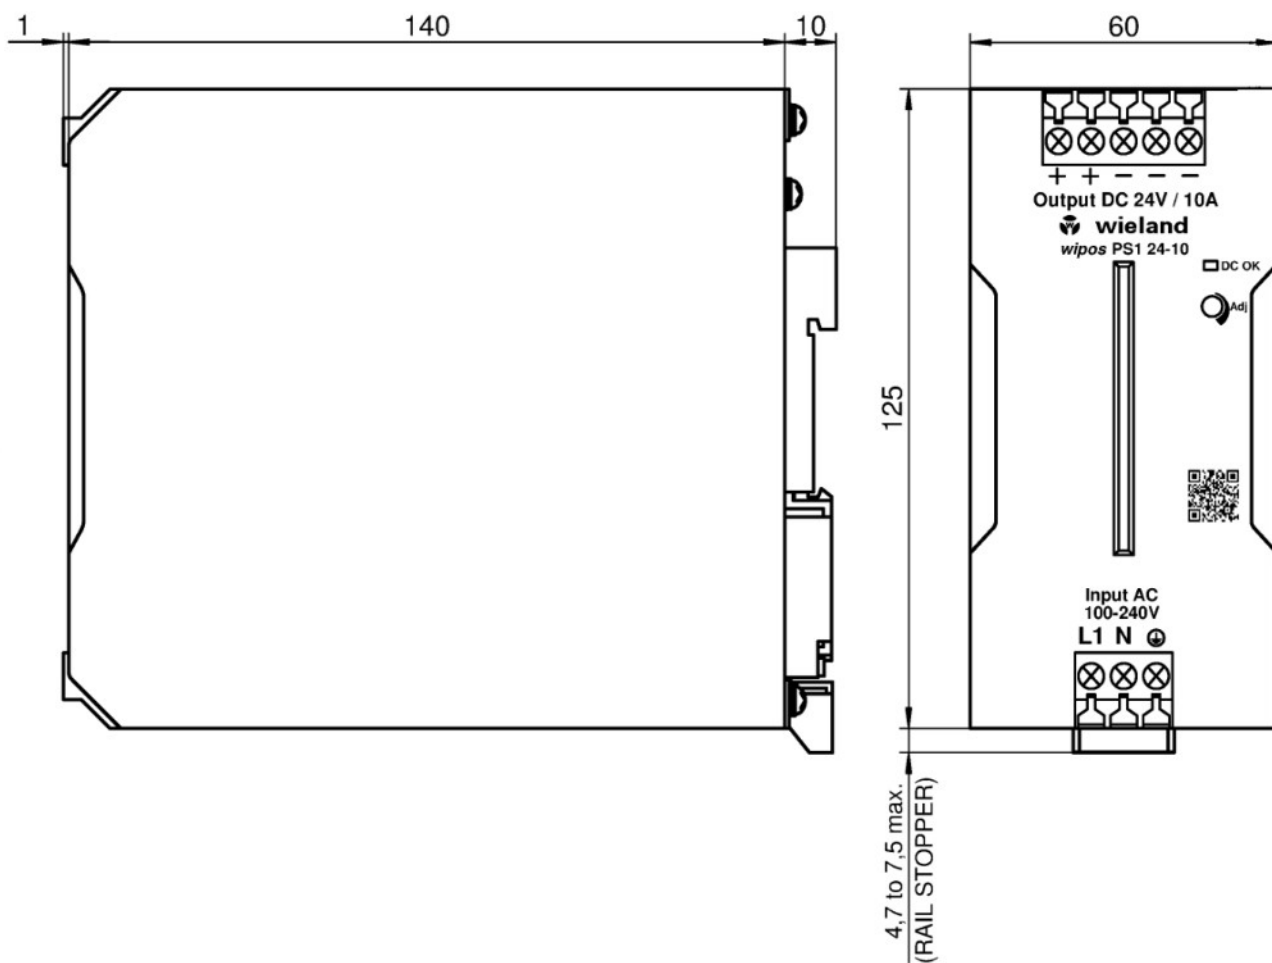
Габаритные и установочные размеры блока питания PS1 24-10
